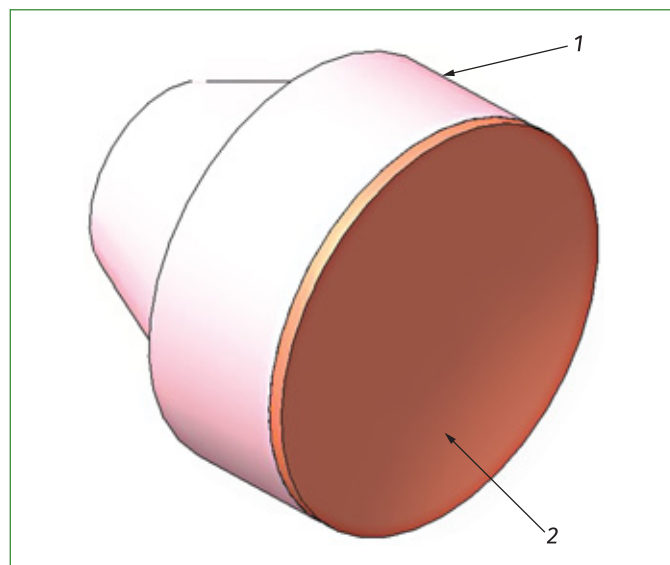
Общий вид разрушителя (без корпуса и устройства позиционирования):
